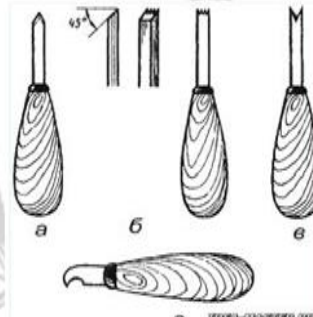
Резцы: а — клепок; б — рифелек; в — циркуль; г — коготок.
